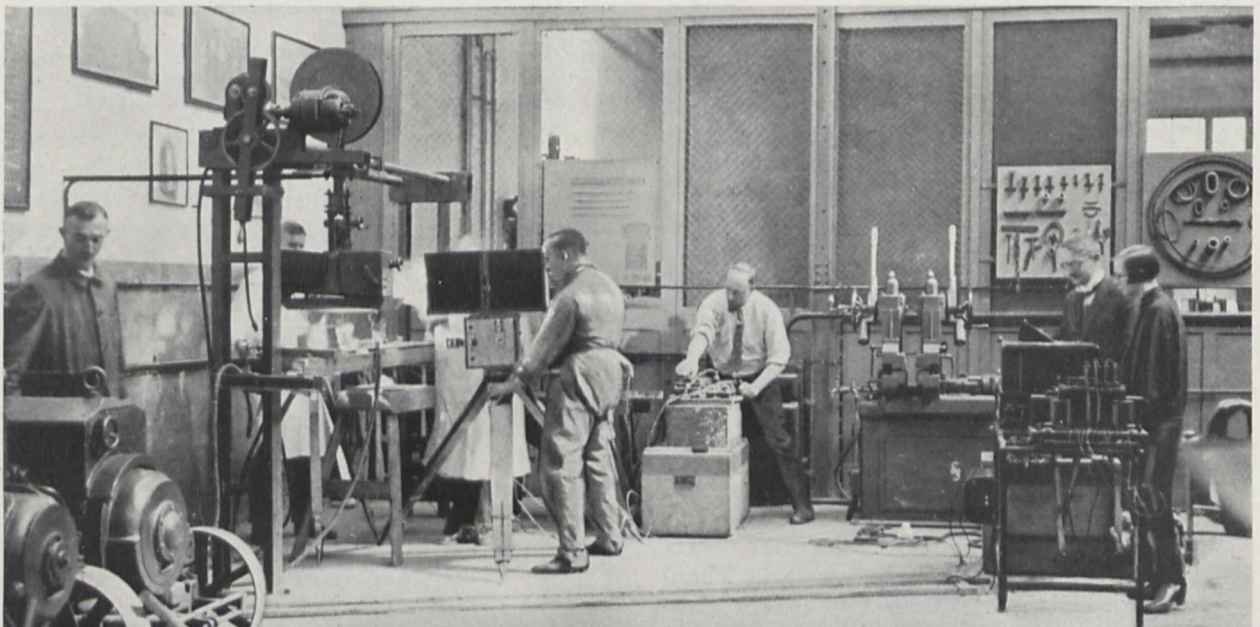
Der Zeitdehner bei der Aufnahme am Schweißautomaten.
